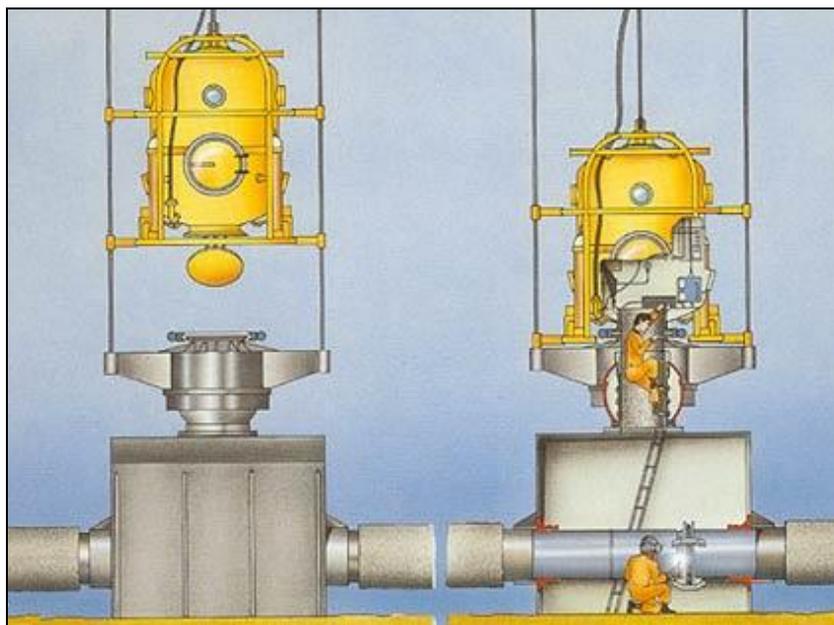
Soudage en condition hyperbare (doc. Internet)
